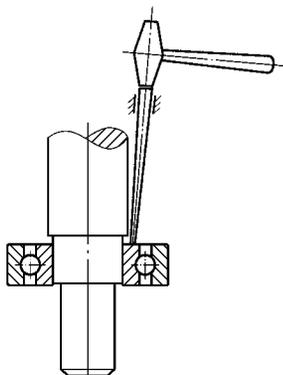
39 通过冲子击打滚动轴承的拆卸方法
